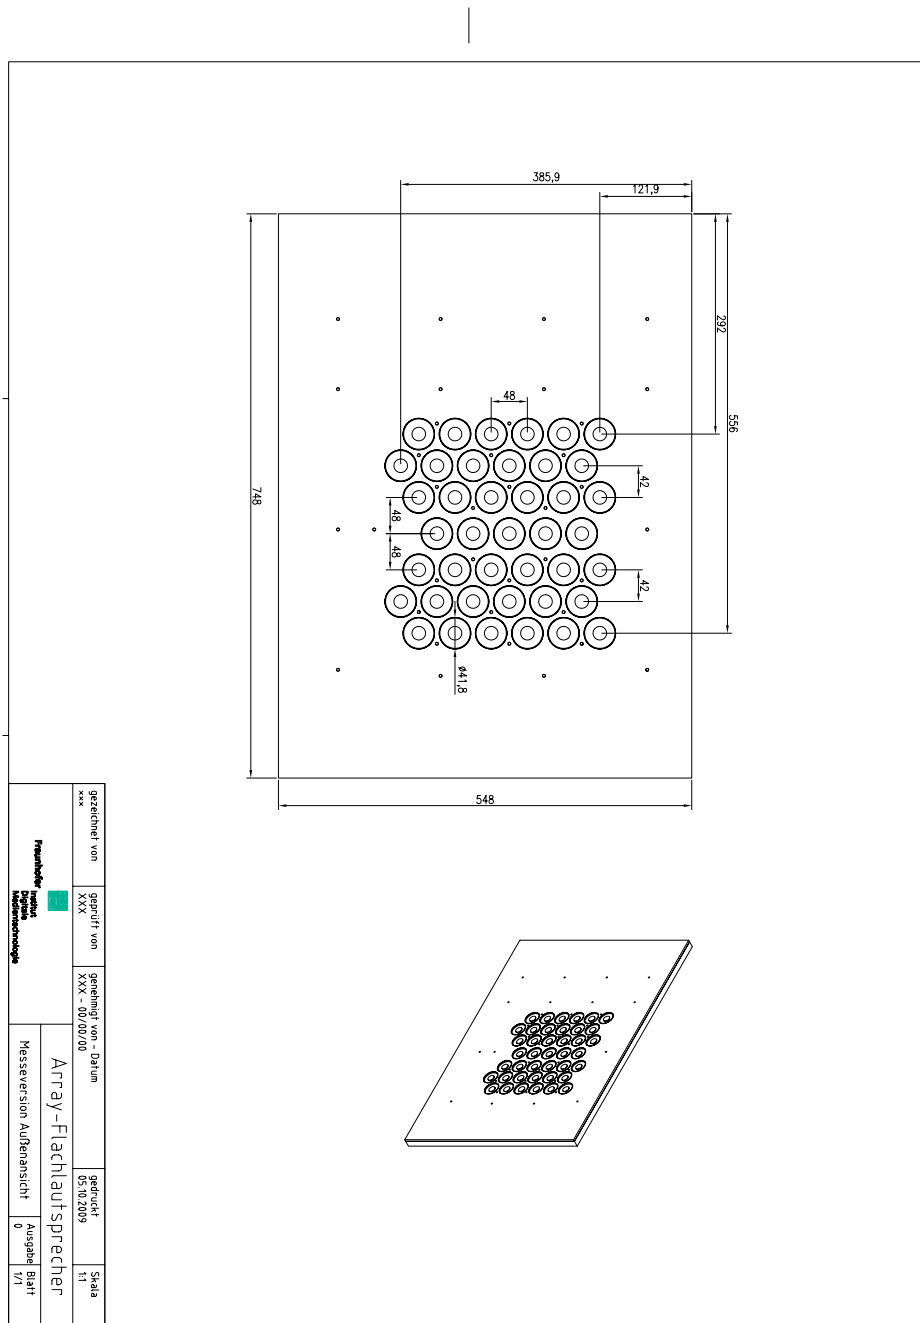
Konstruktionszeichnungen des für die IFA 2009 gefertigten Flachlautsprechers in der Außenansicht
